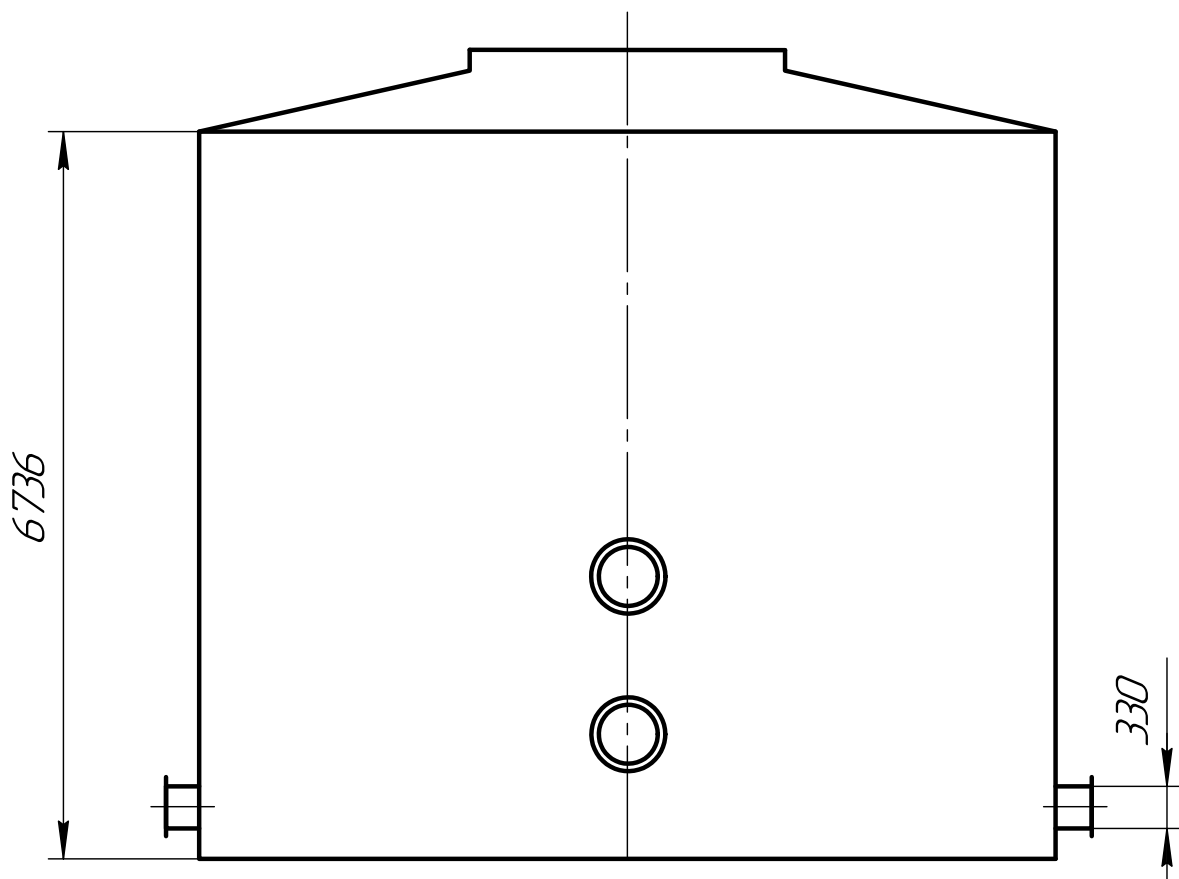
Габаритный эскиз контактного ПГК
